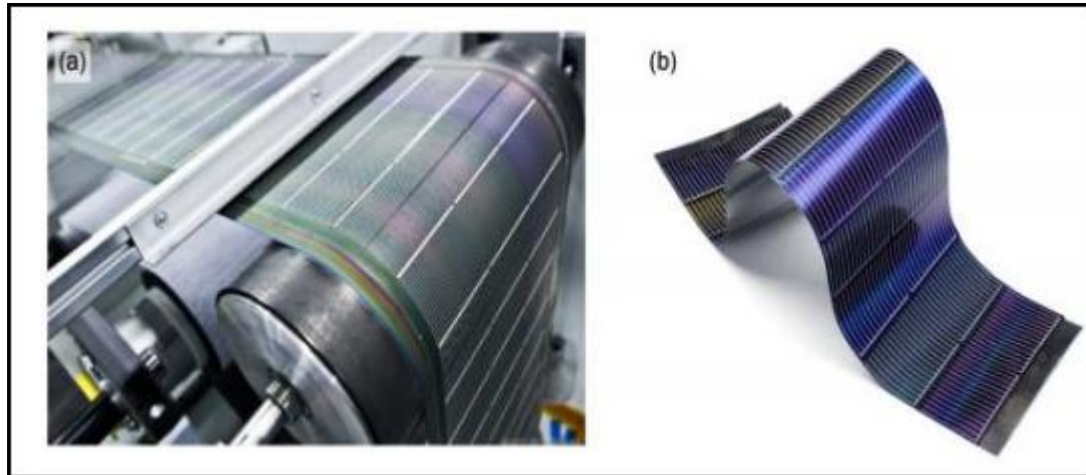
a) Fabrication de cellules en couches minces par procédé roll-to-roll.
